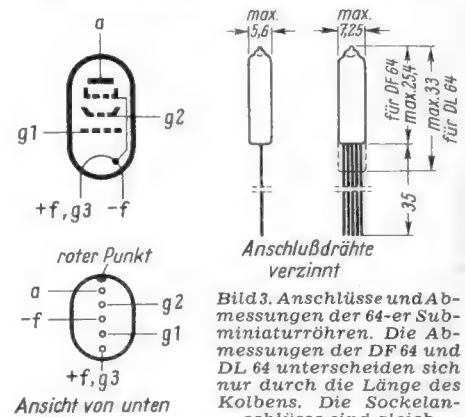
Anschlüsse und Abmessungen der 64-er Subminiaturröhren. Die Abmessungen der DF 64 und DL 64 unterscheiden sich nur durch die Länge des Kolbens. Die Socketanschlüsse sind gleich
